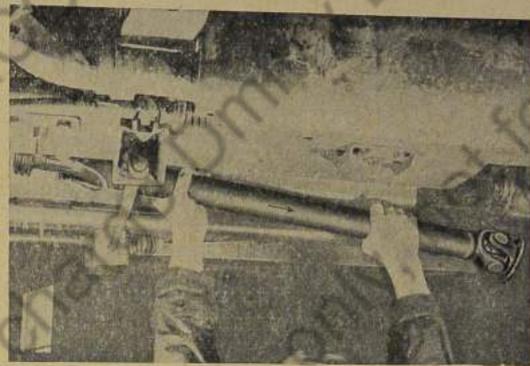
Hintere Längsgelenkwelle aus Keilnabenprofil herausziehen
